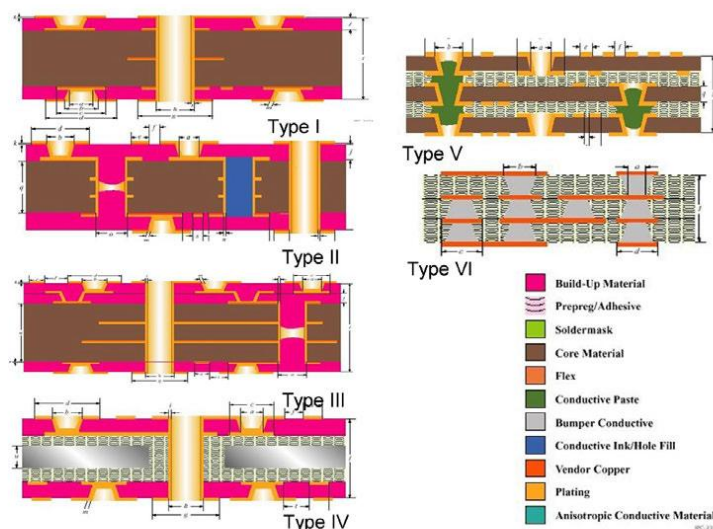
以 HDI 基礎製程技術所衍伸之多種類型 PCB
